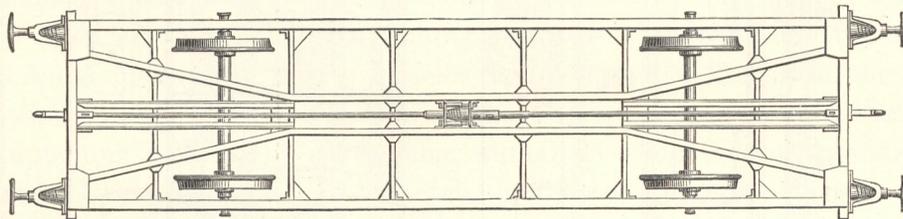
Untergestell mit zwei Achsen und festem Radstand (Grundriß).
